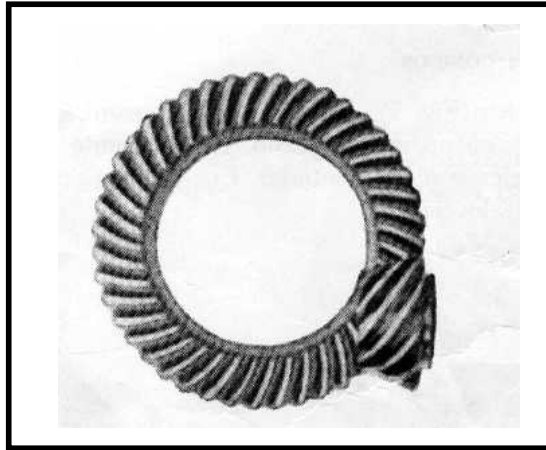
ENGRANAJES CÓNICO-HIPOIDES
